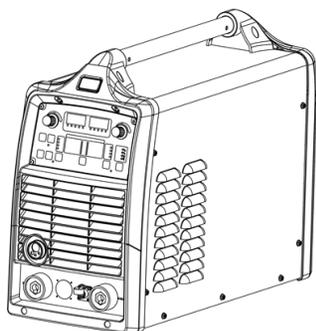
Комплект для аргонодуговой сварки
